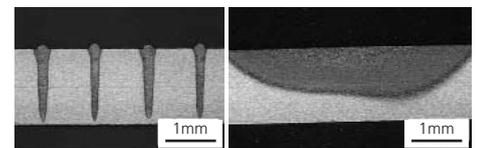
Querschliffe von Faserlaserschweißnähten (links) und einer HLDL-Härtespur (rechts)
